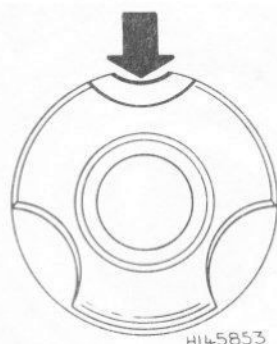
Le cran des bagues de fixation de suspension arrière (fléché) doit se trouver dans le plan vertical (Sec 15)
